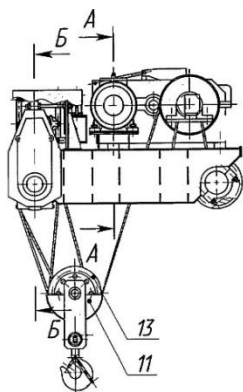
Общий вид грузовой тележки: 11 – грузозахватный орган; 13 – блок
